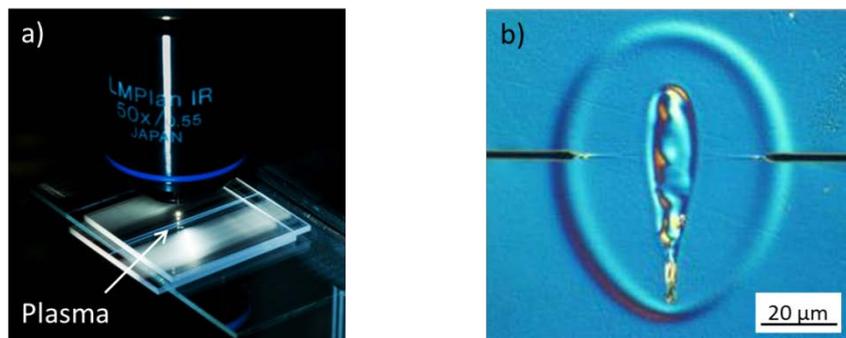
Glasschweißen mit UKP-Lasern: a) Erzeugung von Plasma in Glas durch Multiphotonenabsorption und b) geätzter Querschliff einer Glasschweißnaht
